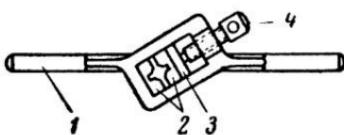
Косой клупп. 1 — клупп; 2 — плашки; 3 — сухарь; 4 — регулировочный винт.
